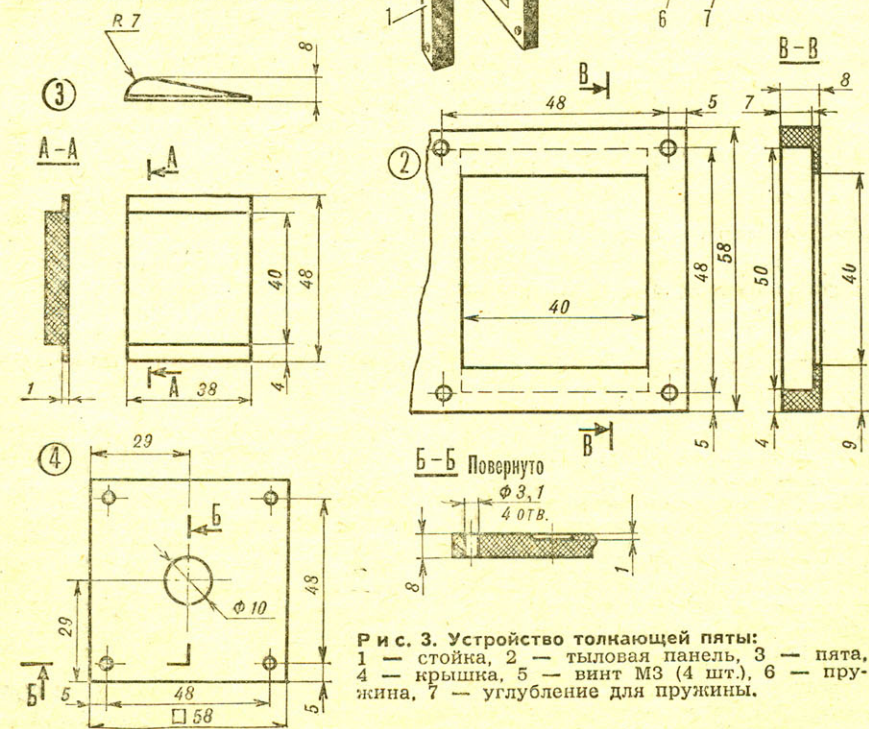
Устройство толкающей пяди: 1 — стойка, 2 — тыловая панель, 3 — пята, 4 — крышка, 5 — винт М3 (4 шт.), 6 — пружина, 7 — углубление для пружины.
